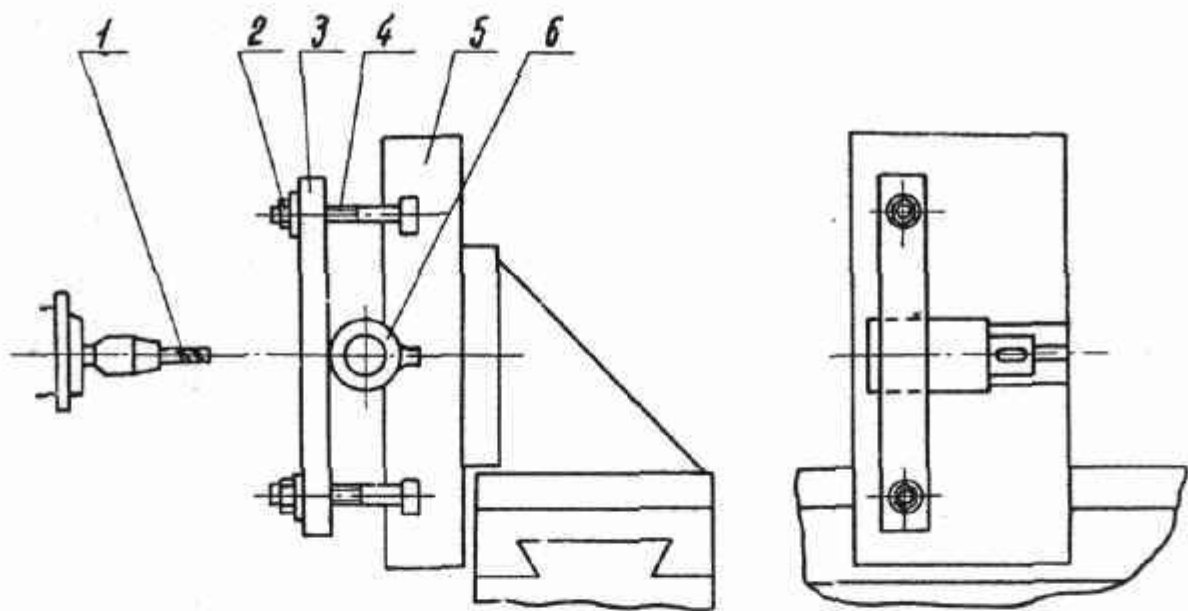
Схема фрезерования глухих шпоночных пазов во фрезерном приспособлении
